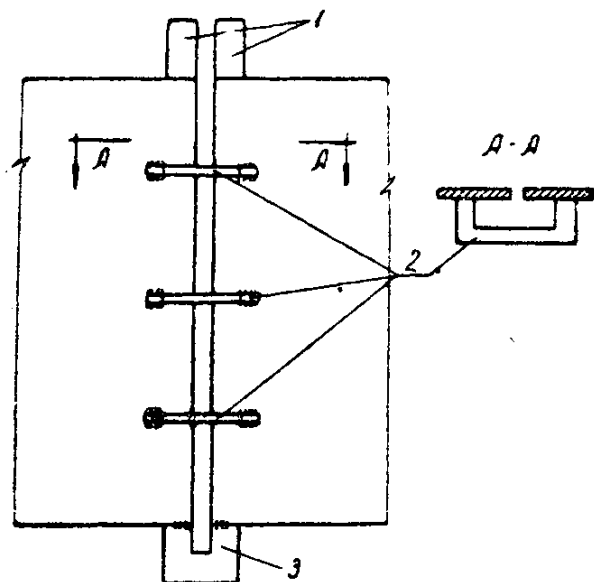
Установка сборочных скоб и выводных планок при электрошлаковой сварке: 1 — верхние выводные планки; 2 — сборочные скобы; 3 — нижняя выводная планка с карманом.
